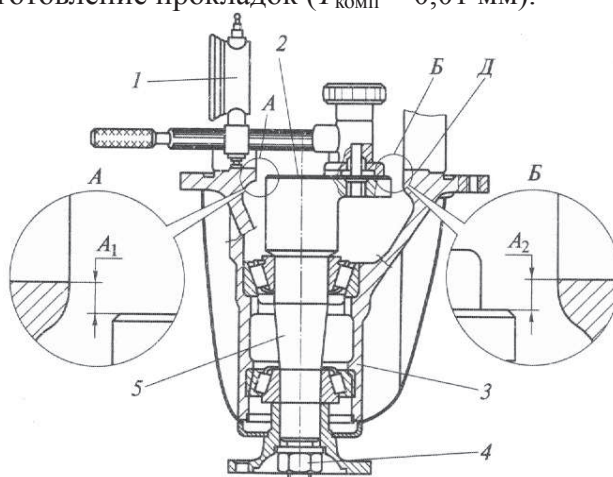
Схема определения толщины регулировочной прокладки (кольца) ведущего колеса: 1 – индикатор приспособления; 2 – торец оправки; 3 – корпус редуктора; 4 – гайка; 5 - оправка; Д – посадочные поверхности подшипников дифференциала; A_1 и A_2 – расстояние от торца оправки до нижних точек посадочных поверхностей подшипников дифференциала
